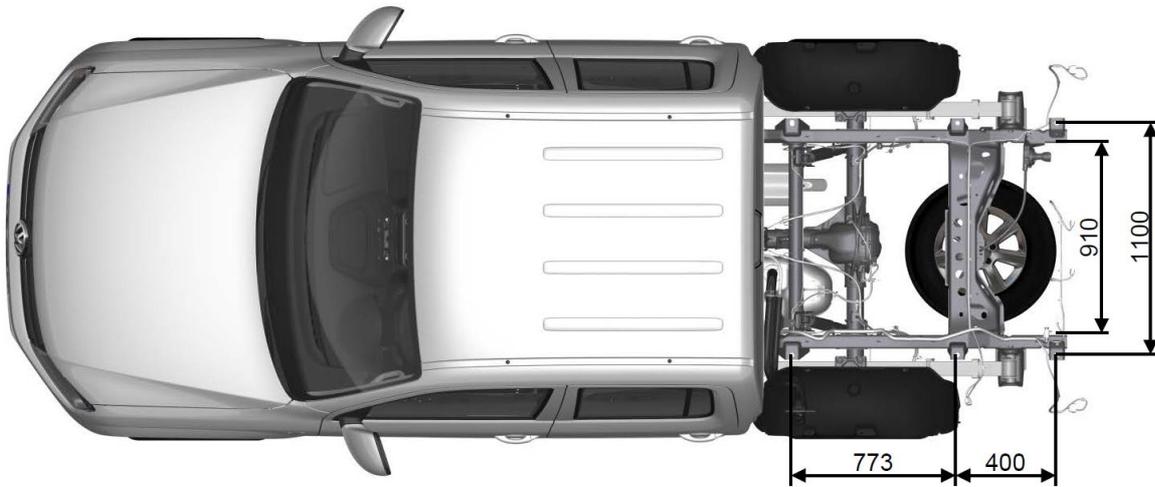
Vista de planta Amarok DC sin Cargobox
